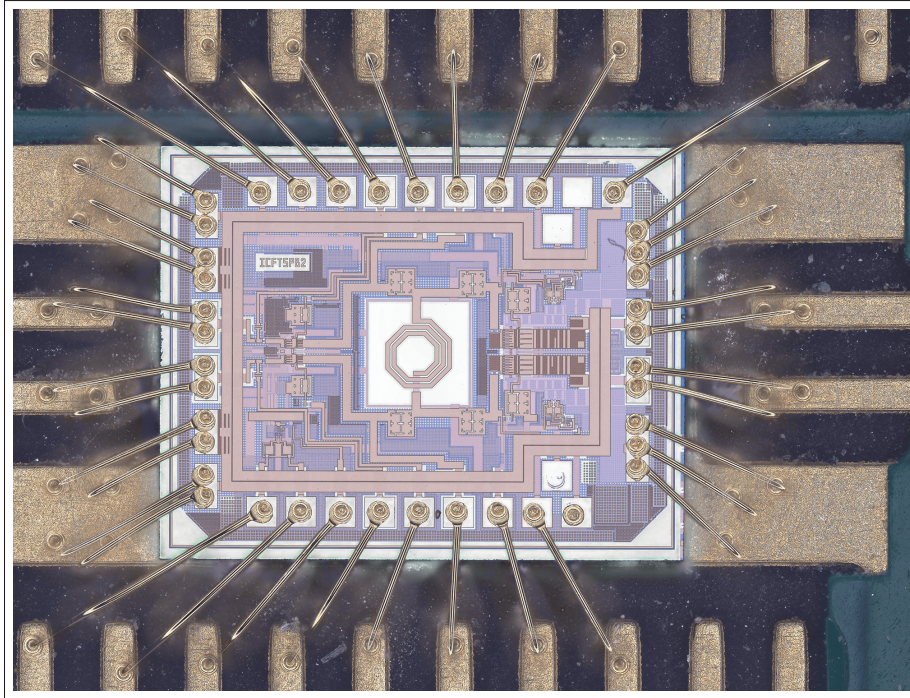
Photographie de la puce ICFTSPB2 montée sur le PCB avec les fils d'or
